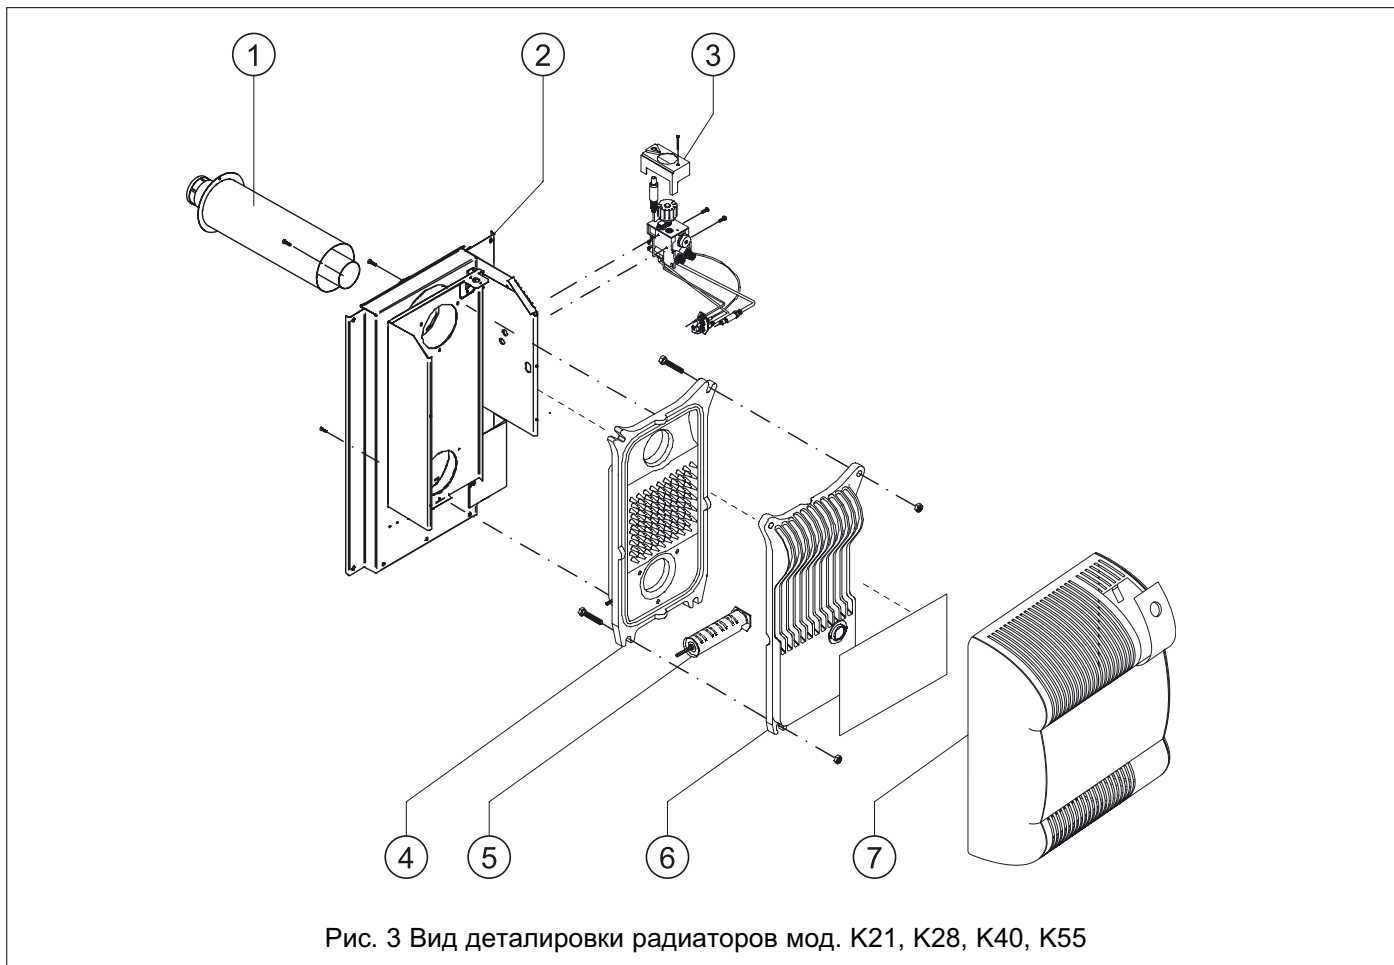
Вид детализовки радиаторов мод. K21, K28, K40, K55
